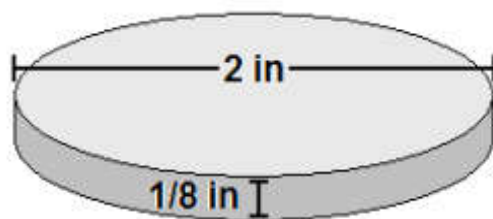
Forma y dimensiones de blanco fabricado para el equipo de erosión catódica.
